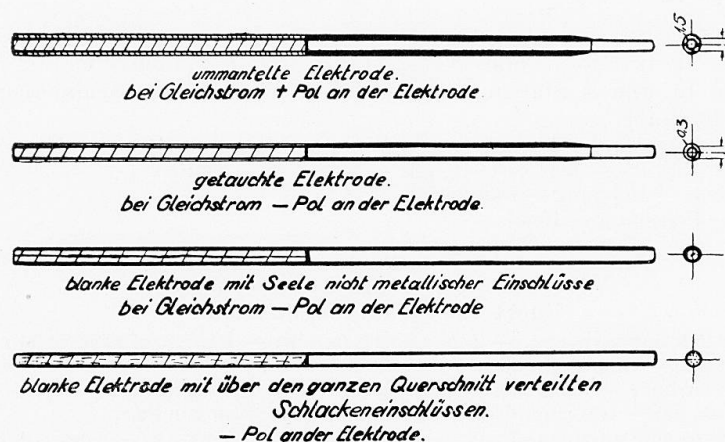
Electrodes pour soudure d'assemblage
